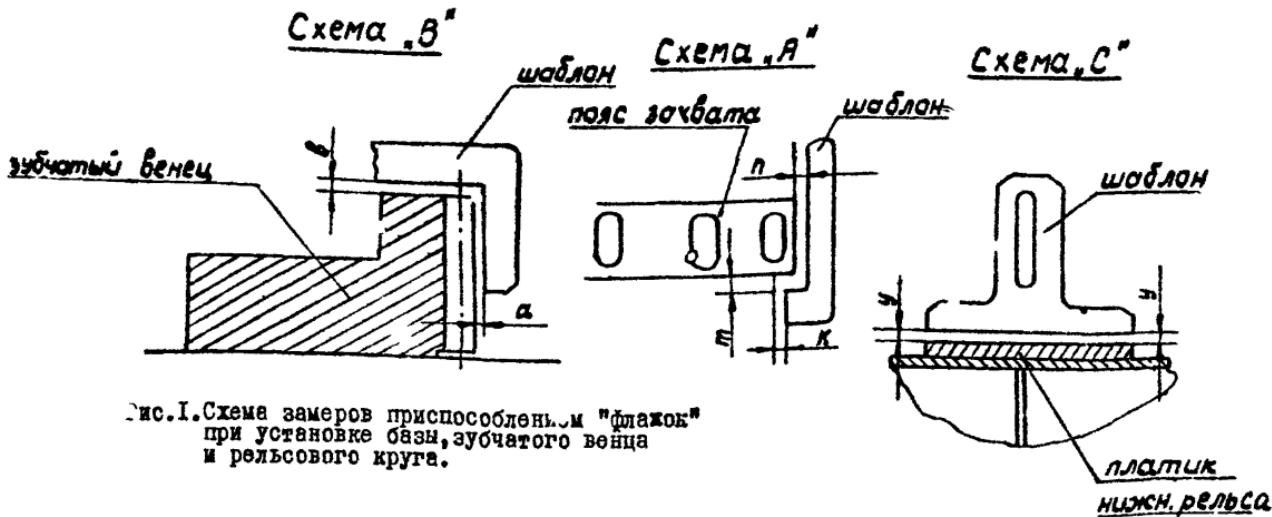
Рис. I. Схема замеров приспособлением "флажок" при установке базы, зубчатого венца и рельсового круга.
